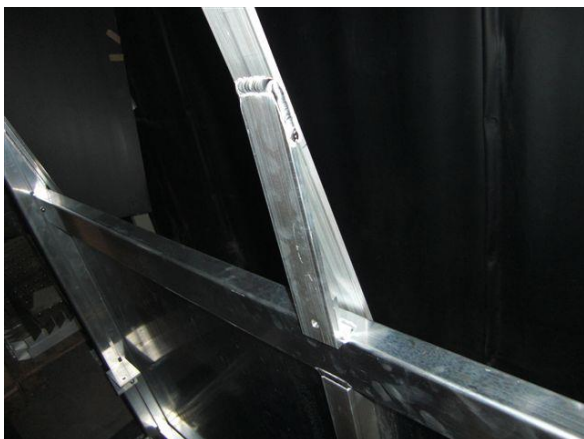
Dach-Mittelbögen mit der angeschweißten Lasche mittels Linsenkopfschrauben DIN 7380 M8x16 an die Rückwand schrauben (bei 3m-Kabine 2 Stück; bei 4m-Kabine 3 Stück; bei 5m-Kabine 4 St.).
